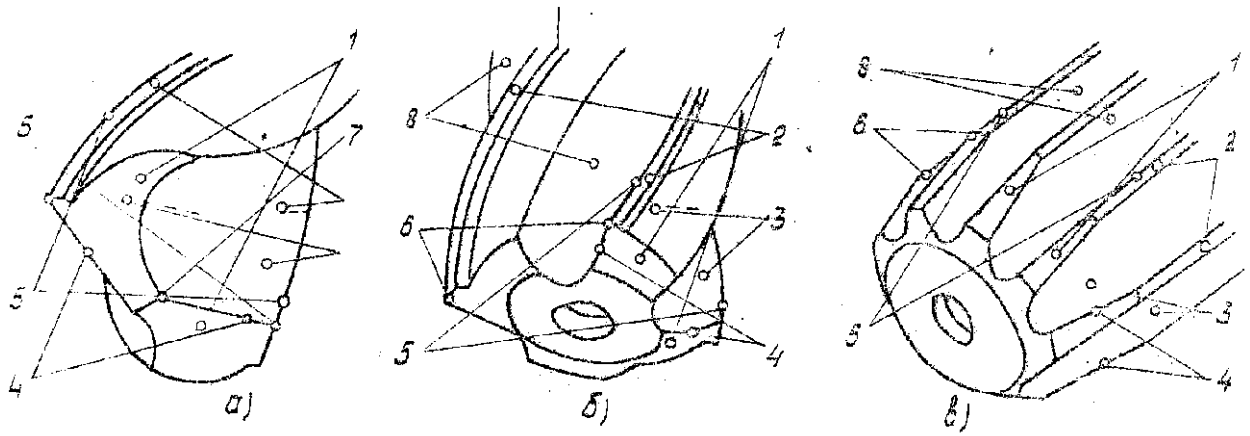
Элементы режущей части сверла (а), зенкера (б) и развертки (в).
